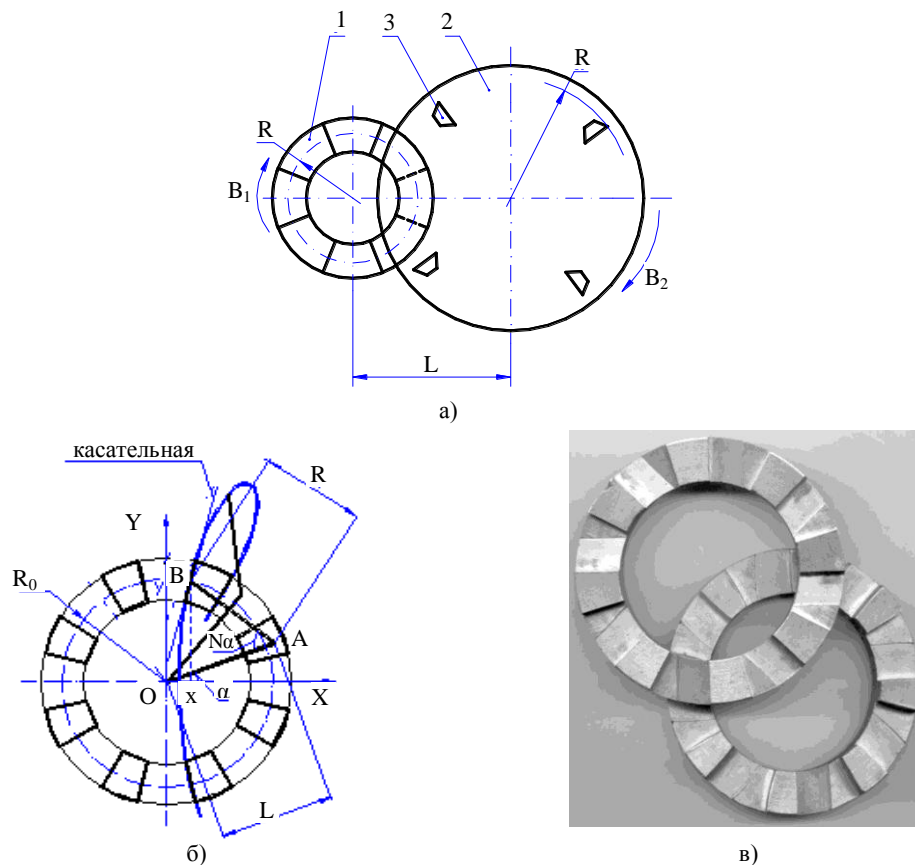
Схема обработки (а), графическая модель формообразования (б) и образцы обработанных деталей (в) с ТЗК
